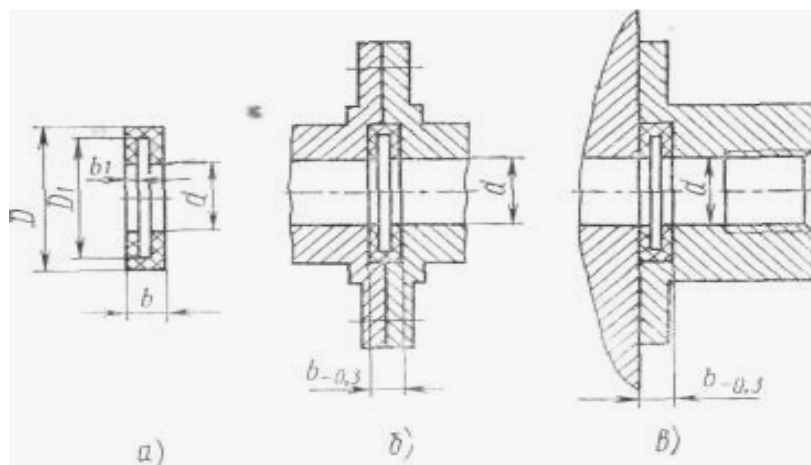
Конструкция и способы установки уплотнительных манжет П-образного сечения:
